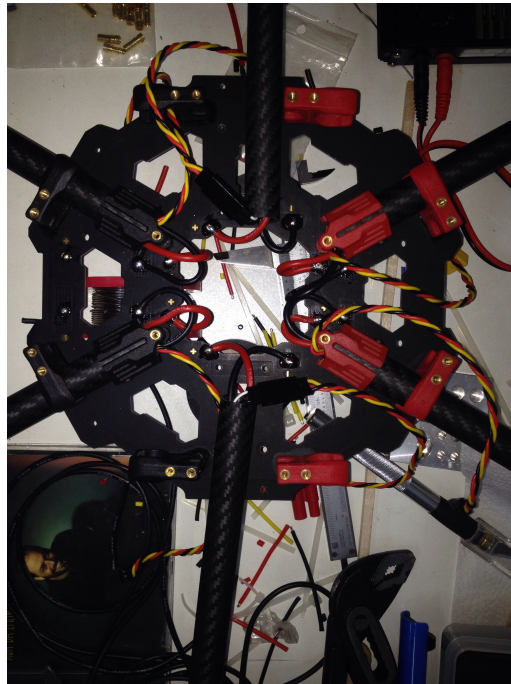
Soldadura da cablagem de potência e passagem de cabos de sinal.
